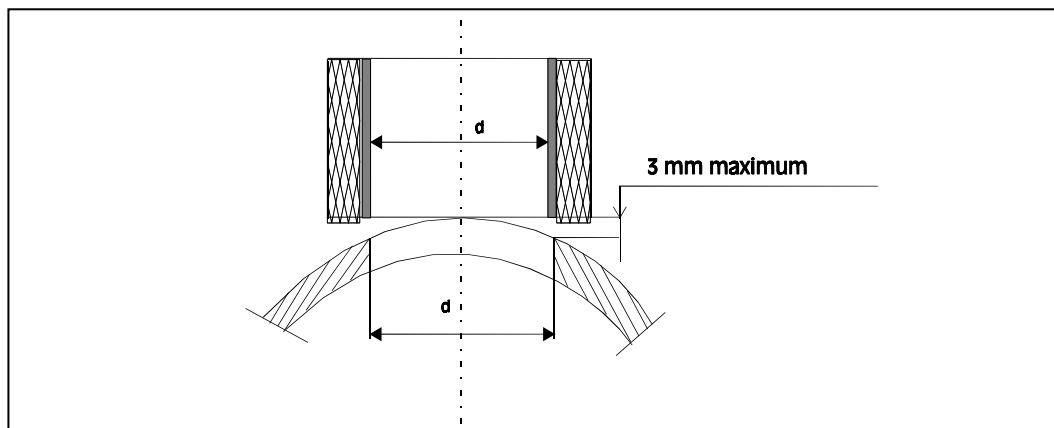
β : Préparation des éléments pour soudure en jonctions latérales
